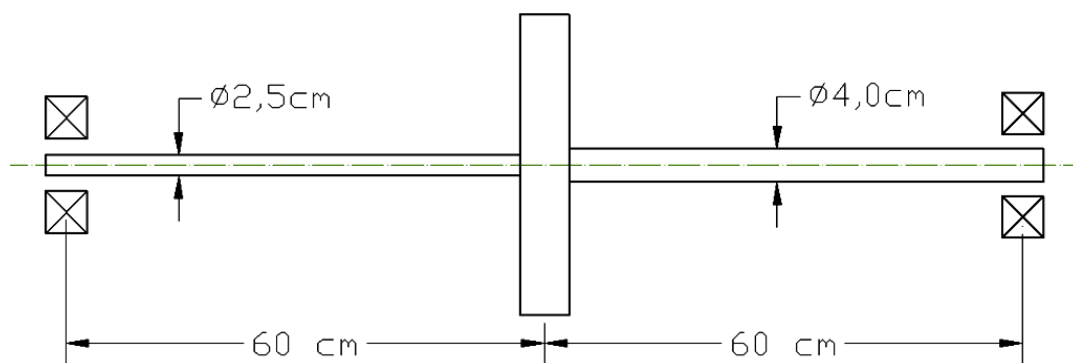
Desenho esquemático do rotor de Hong e Park(1999)
